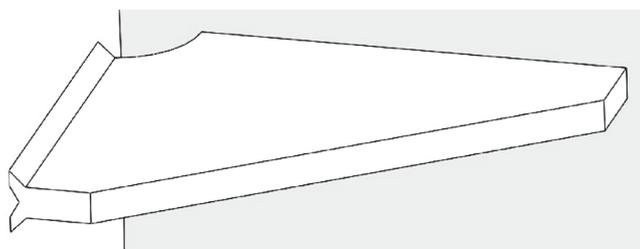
Сварной автоматический шов без разделки кромок
